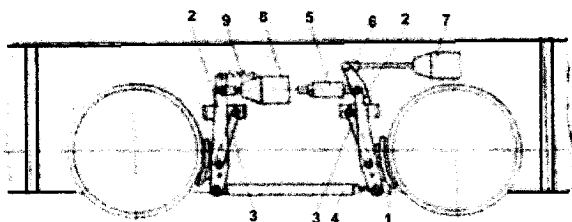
Механическая тормозная система электровоза КТ14: 1 – четыре колодки; 2 – рычаги; 3 – рычаги; 4 – тяга; 5 – пружинный демпфер; 6 – рычаг; 7, 8 – пневмоцилиндры; 9 – пружина.
